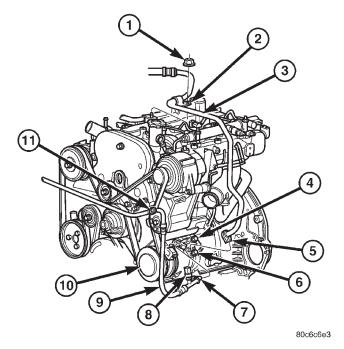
COMPRESOR DE A/A - MOTOR 2.5L DIESEL
